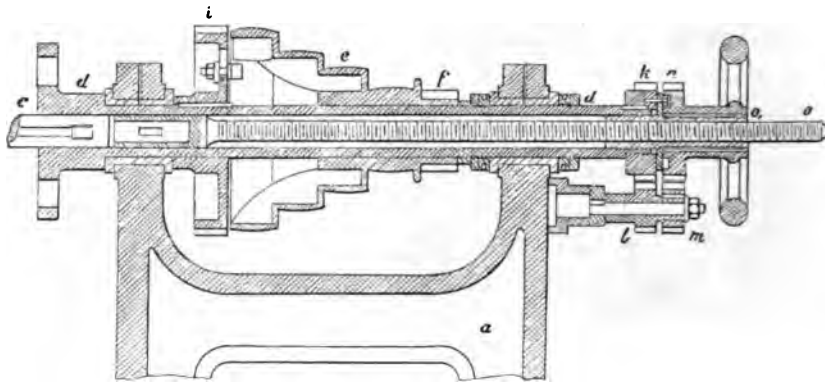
Spindelstock einer Horizontalbohrmaschine.
